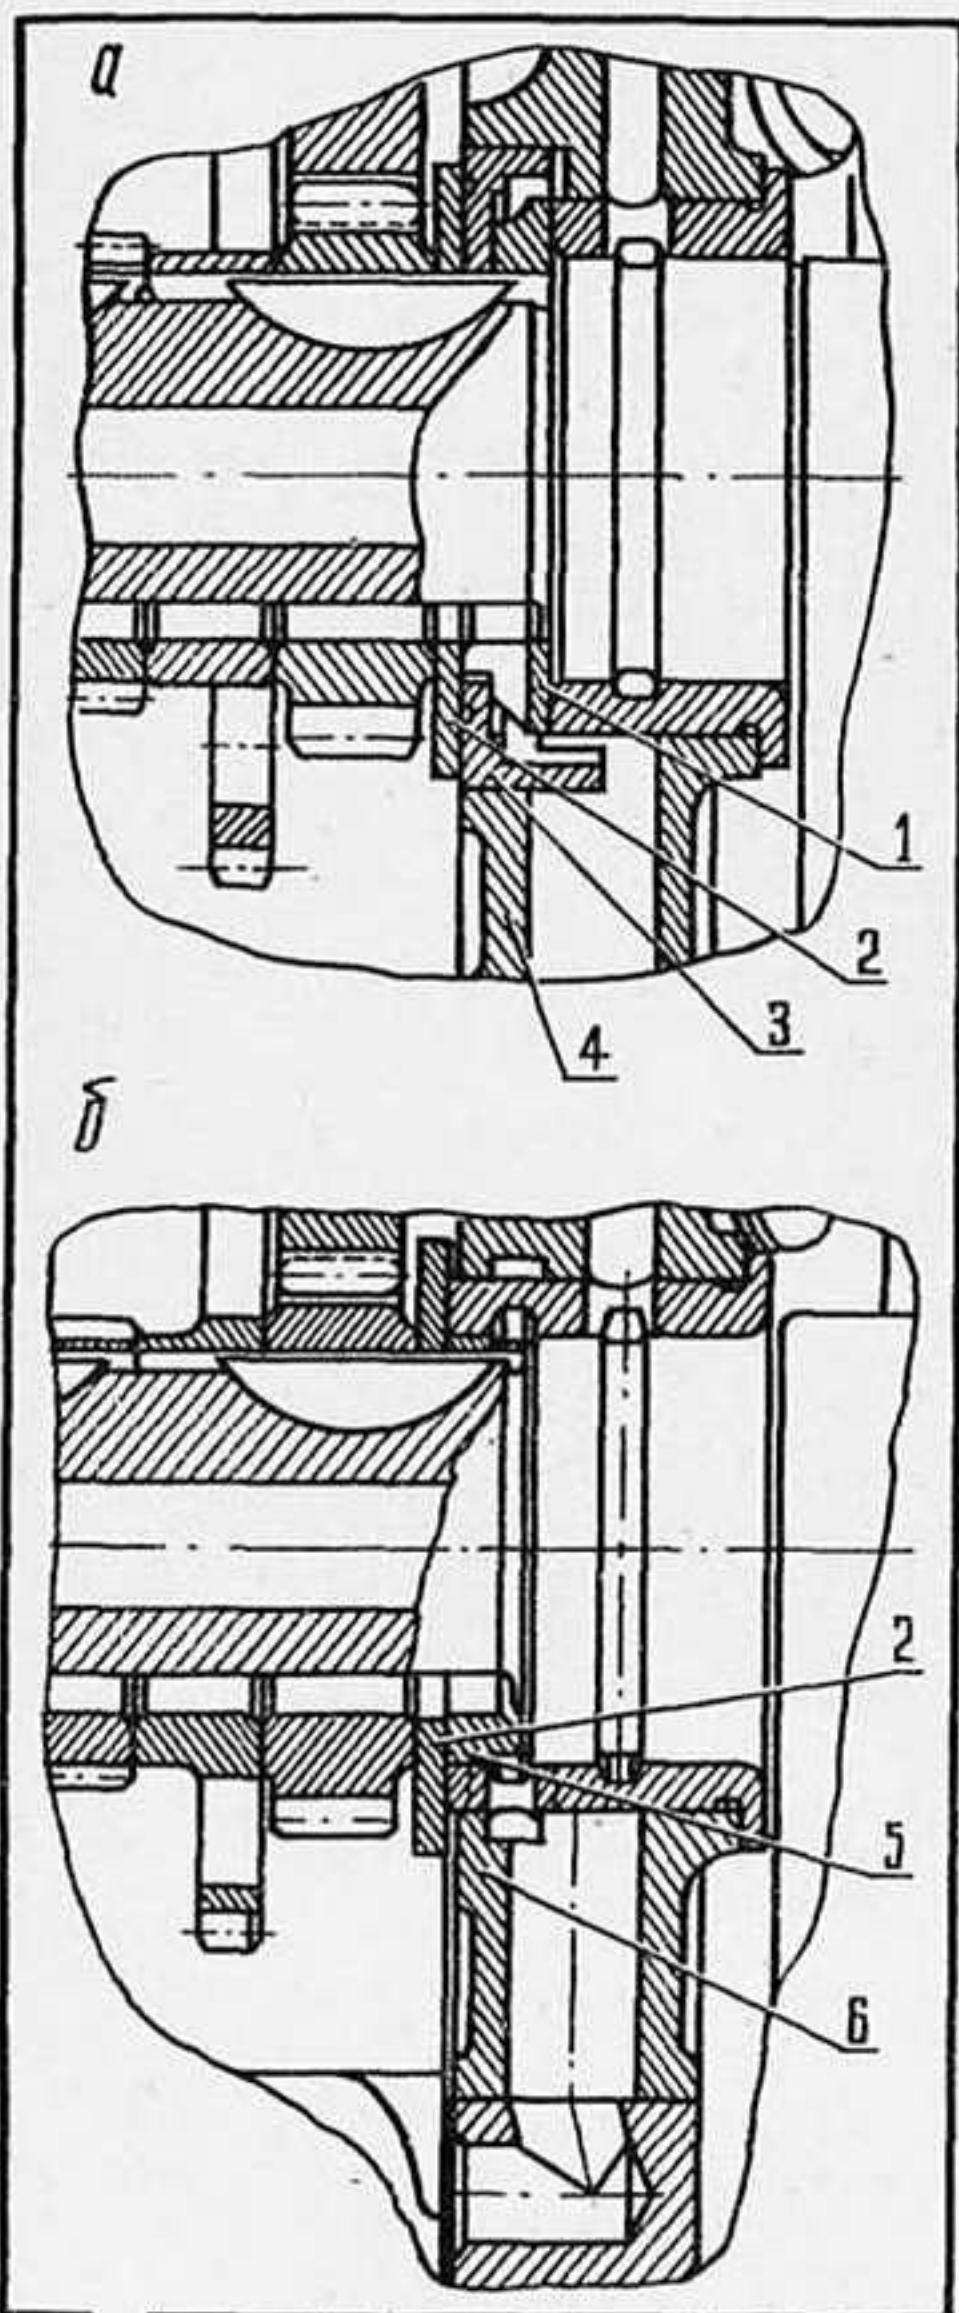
Изменение конструкции передней опоры коленчатого вала: а — было; б — стало: 1 — опорная шайба (деталь 965-1005050); 2 — шайба диска (965-1005047); 3 — диск (965-1005046); 4 — передняя опора в сборе (965-1005080); 5 — упорное кольцо коленчатого вала (965-1005050-Б); 6 — передняя опора в сборе (965-1005080-Б).
